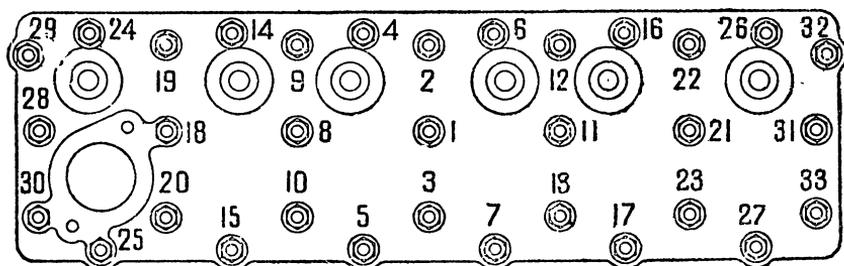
Последовательность затяжки гаек крепления головки блока цилиндров
